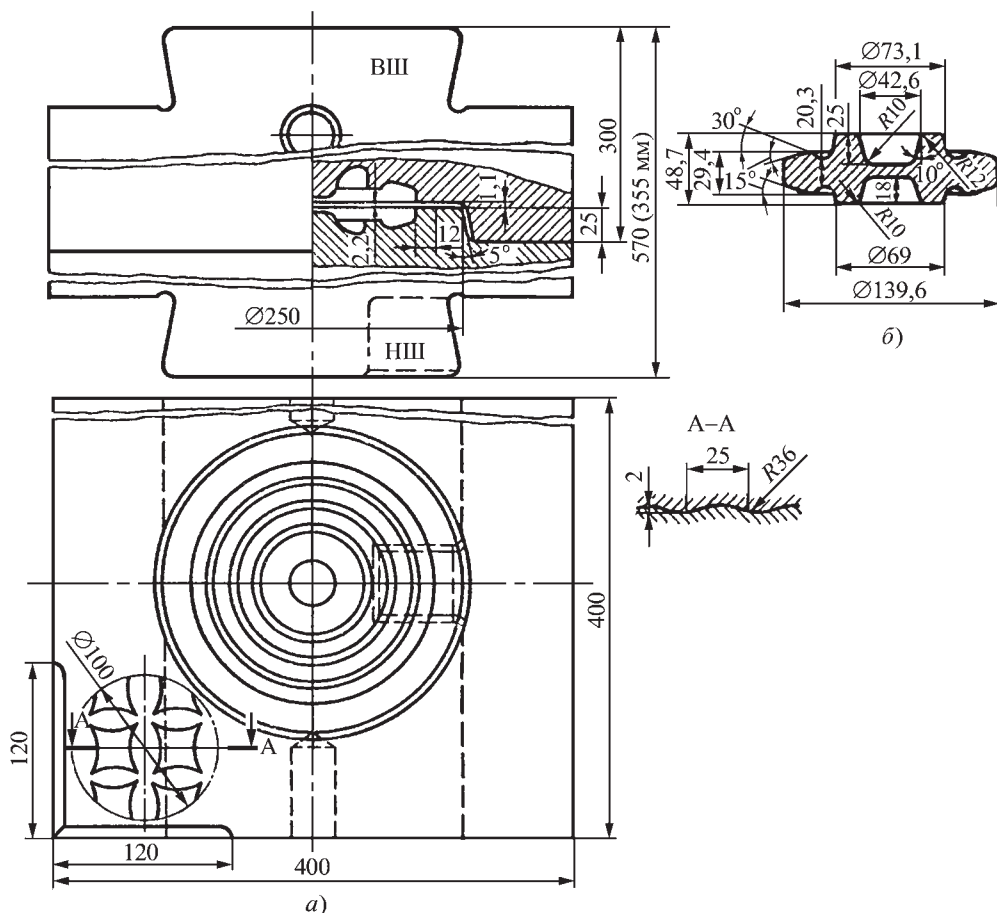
Молотовый штамп (а) и горячая поковка (б) шестерни:
